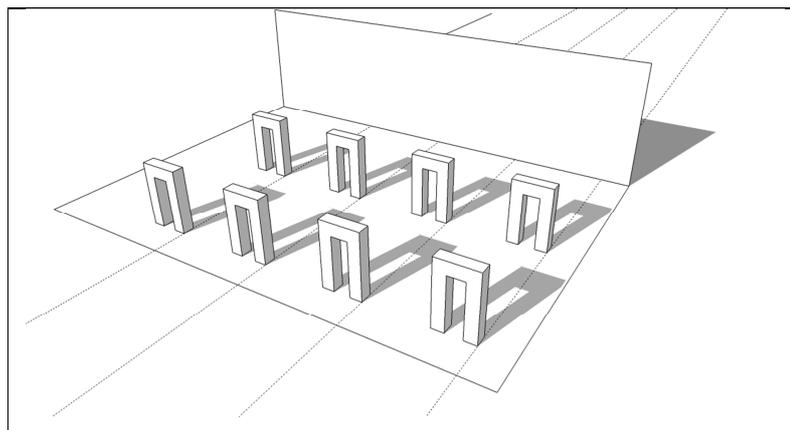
Vista 3D de los ocho (8) bancos de concreto para la colocación de las columnas semiterminadas en la sección de acabado – remate.
